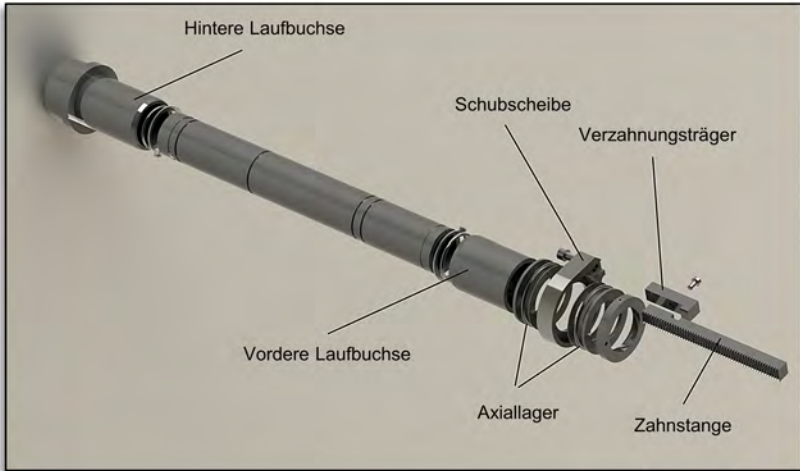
Explosionsansicht des internen Schubgestänges
